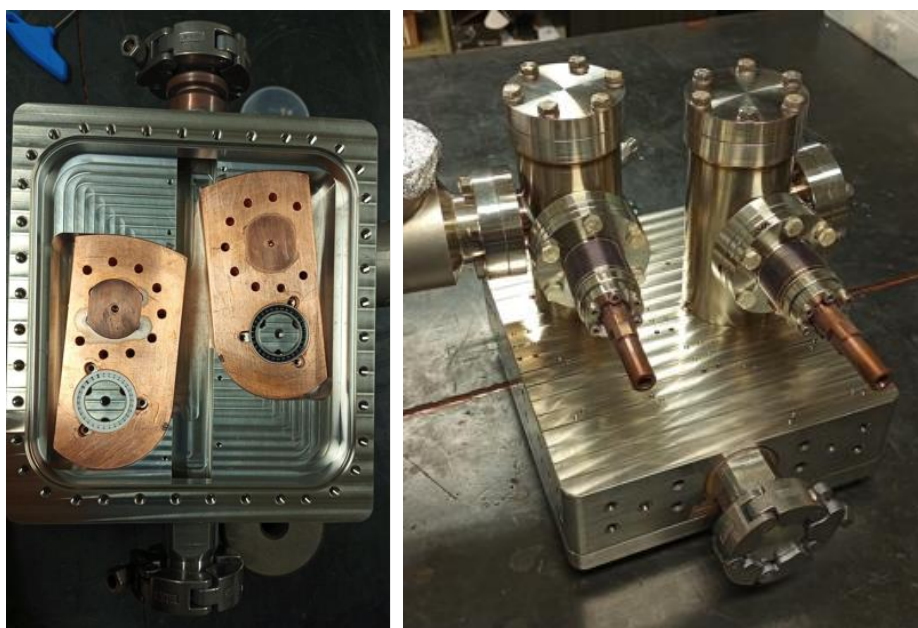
Vista das lâminas de cobre após montagem inicial e *scraper* horizontal montado e em vácuo.
